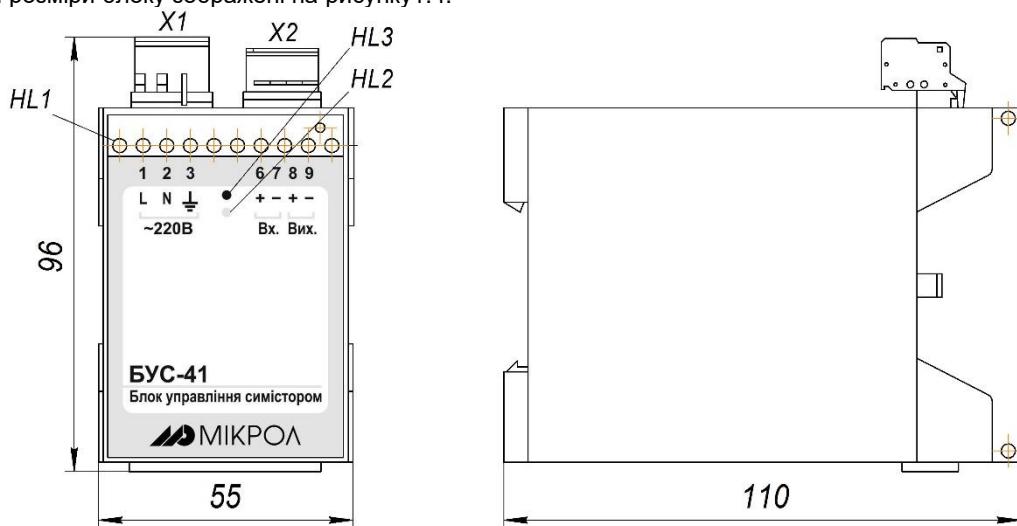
Зовнішній вигляд та габаритні розміри БУС-41
